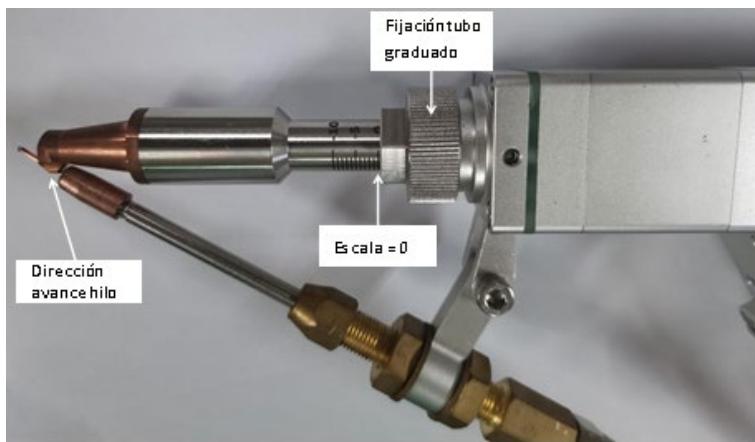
Montaje de la antorcha de soldadura
